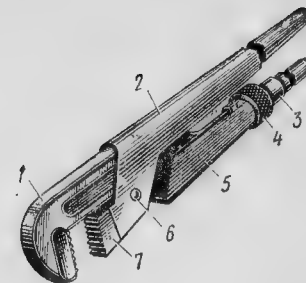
1 — рычаг подвижный; 2 — рычаг неподвижный; 3 — рукоятка; 4 — гайка; 5 — поводок; 6 — ось; 7 — губка
